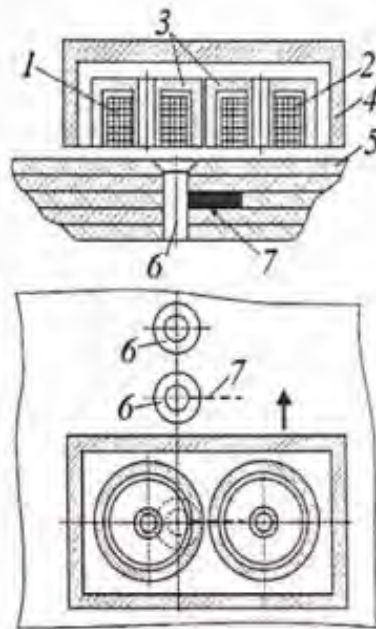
Схема контролю за допомогою ВСП типу SPF-2346: 1 – Обмотка збудження; 2 – Вимірювальна обмотка; 3 – напівброньові осердя; 4 – корпус; 5 – багатощаровий об'єкт контролю; 6 – заклепка; 7 – тріщина
